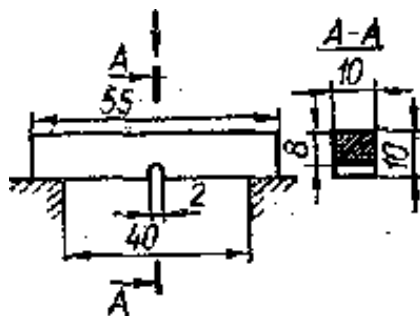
Образец для испытаний с указанием направления удара маятника
